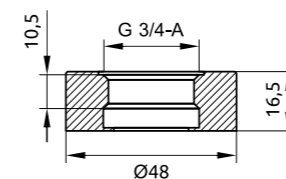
Габаритный чертеж приварного адаптера WA.21-G34-D48-SS6L
